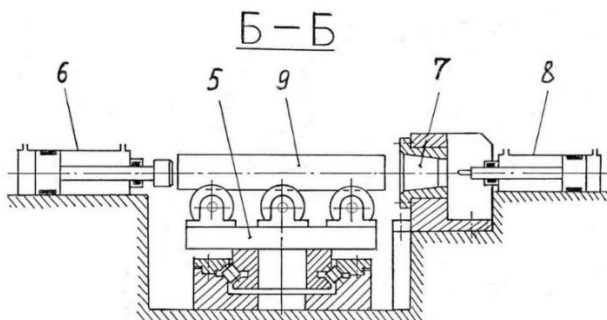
Фронтальний вид на заготовку і обладнання перед пресуванням (розріз Б-Б на рис. 2)
